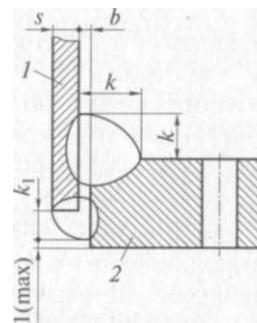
Конструктивные элементы соединения труб с плоскими приварными фланцами:
